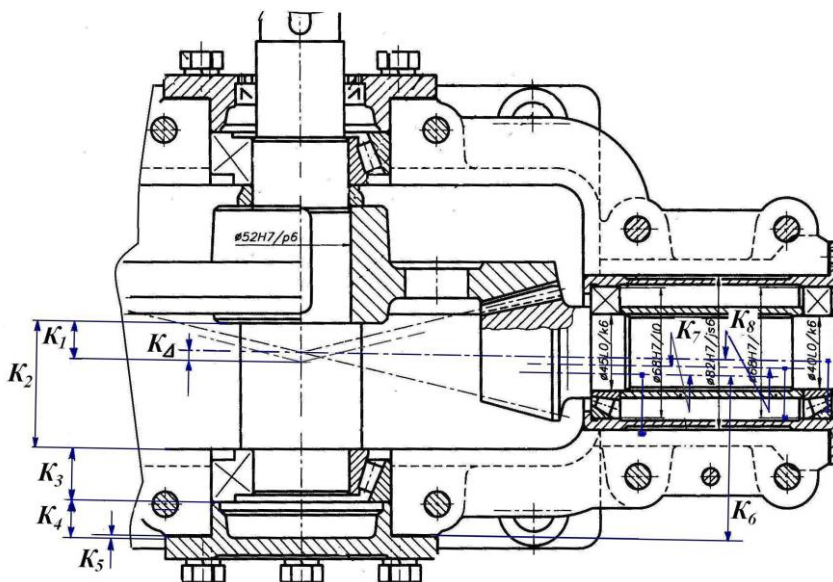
Схема размерной цепи  $K$ , описывающей формирование осевого смещения зубчатого венца конического колеса
